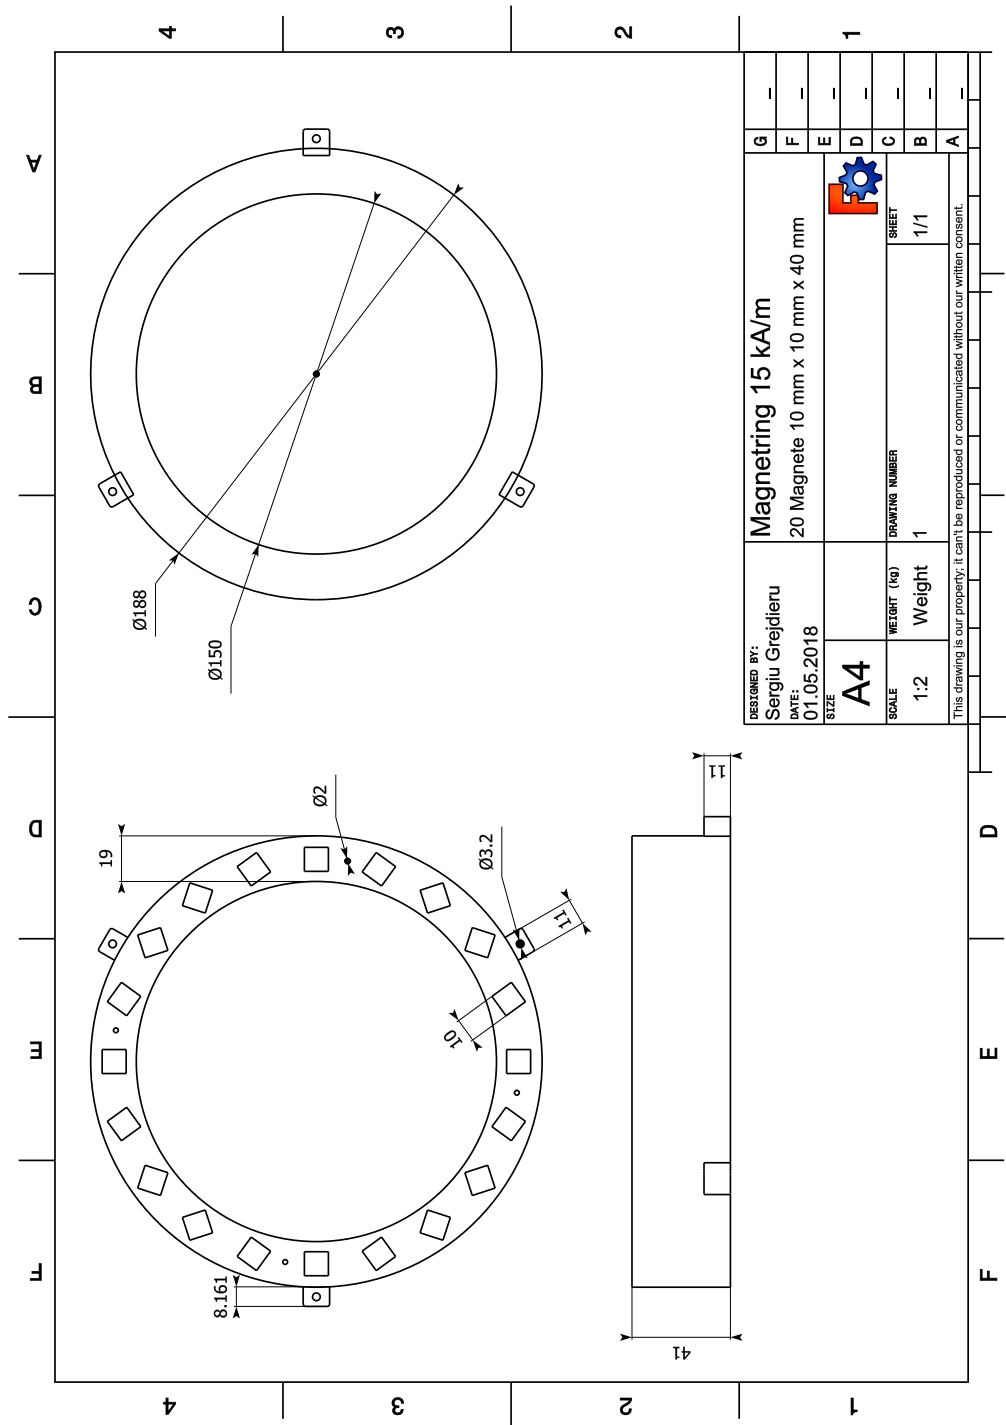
Technische Zeichnung: Magnetring 15 kA/m
